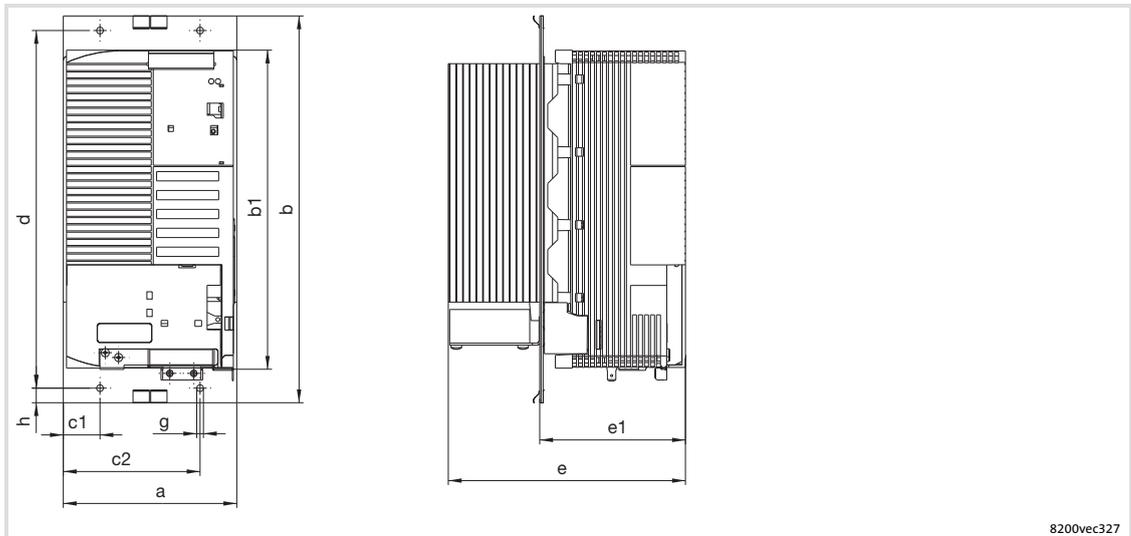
Abmessungen Montage thermisch separiert 3 ... 11 kW
